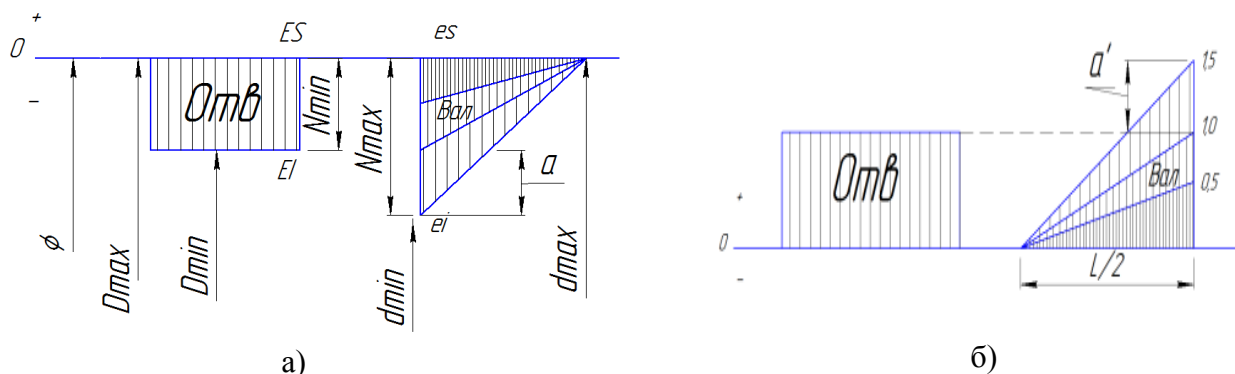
Схема полей допусков для конической пружины
